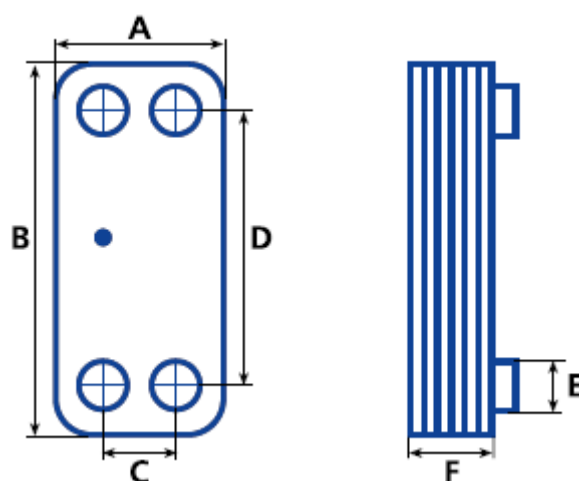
Dimensioni dello scambiatore di calore GEA [23]
